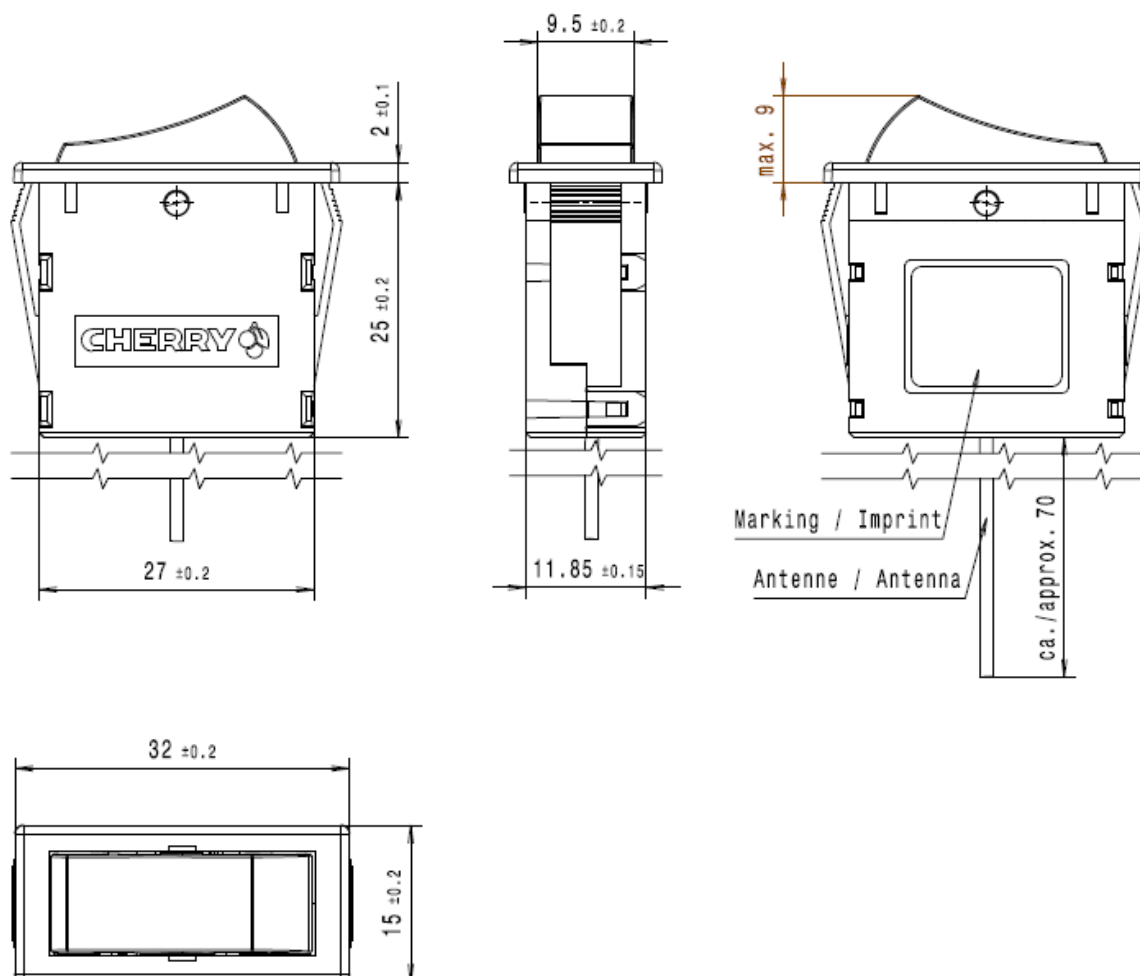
Dimension/Ausführung / Dimension/Version
